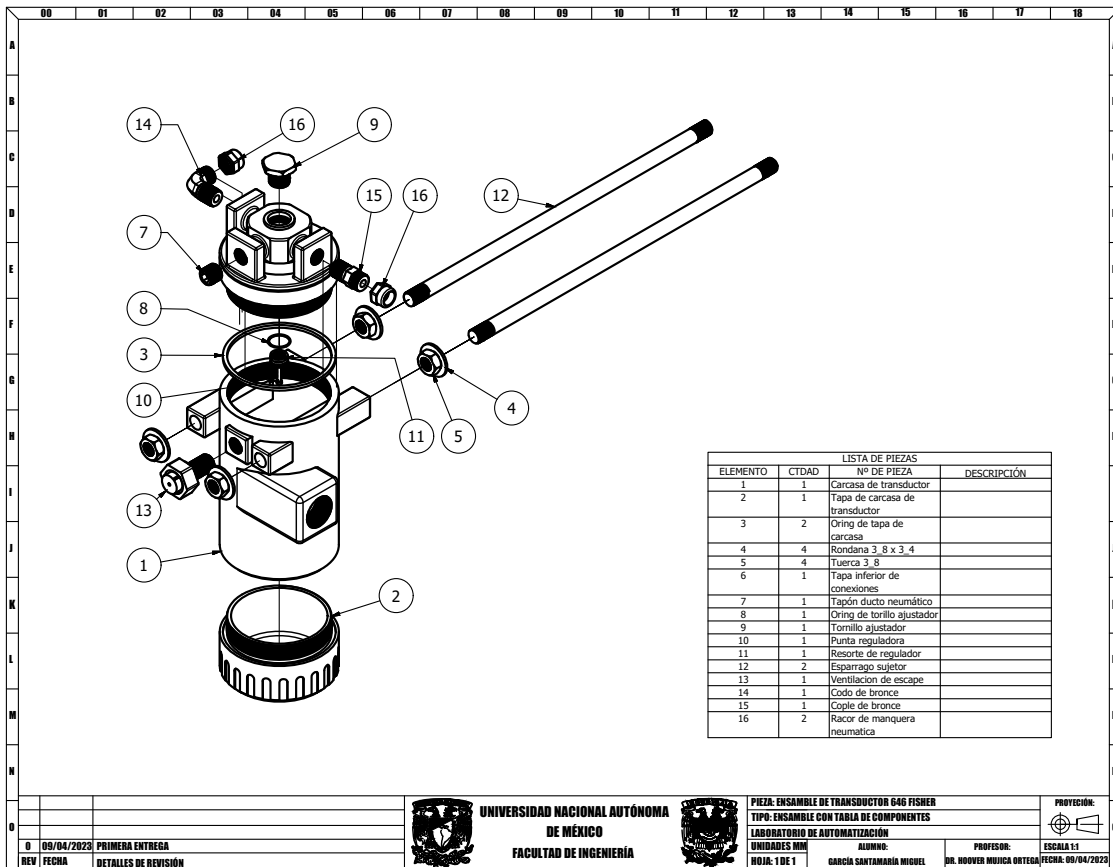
Ensamble explosionado y tabla de componentes de transductor 646 Fisher
